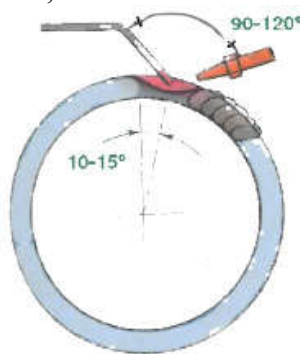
Наложение участка кольцевого сварного шва
